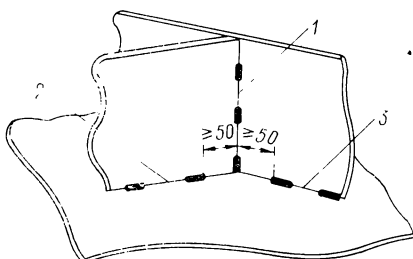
Схема установки прихваток на пересечении сварных соединений.
